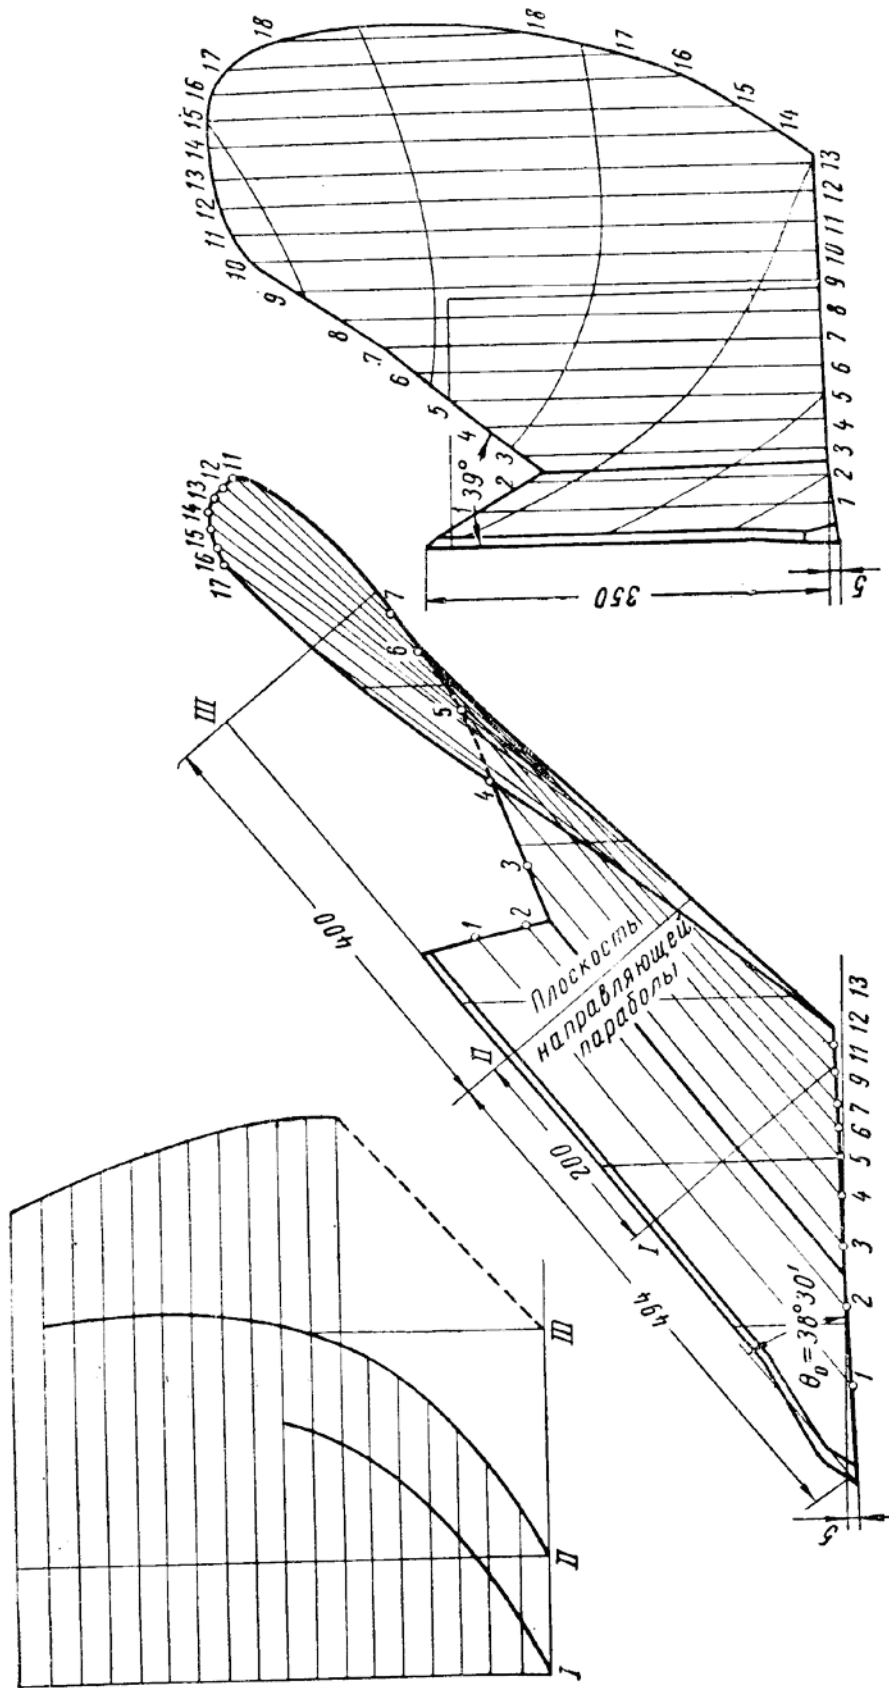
Робоча поверхня напівгвинтового корпусу
